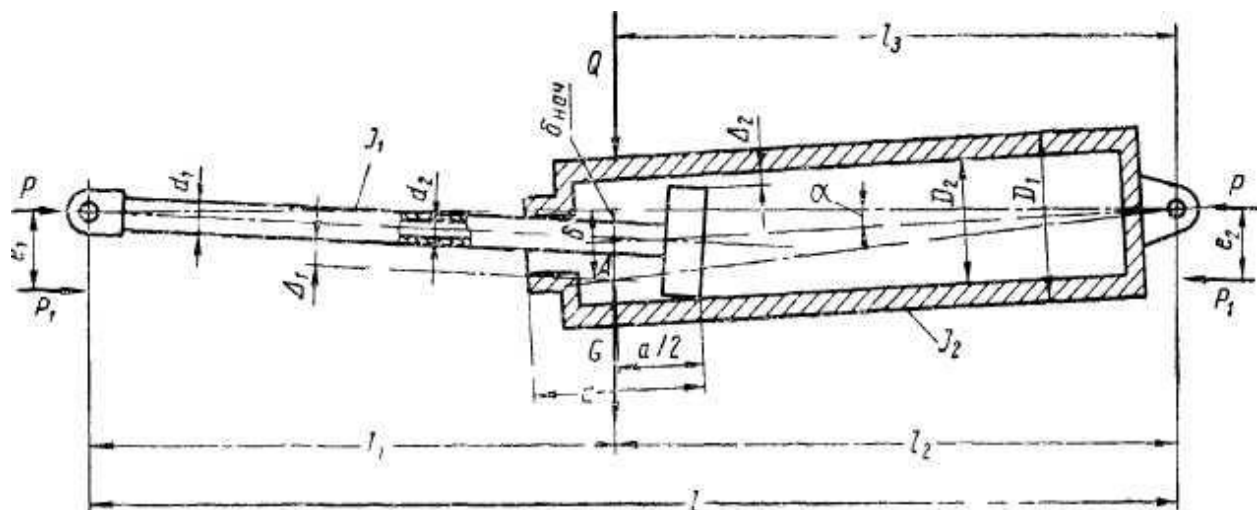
Схема нагружения силового гидроцилиндра
